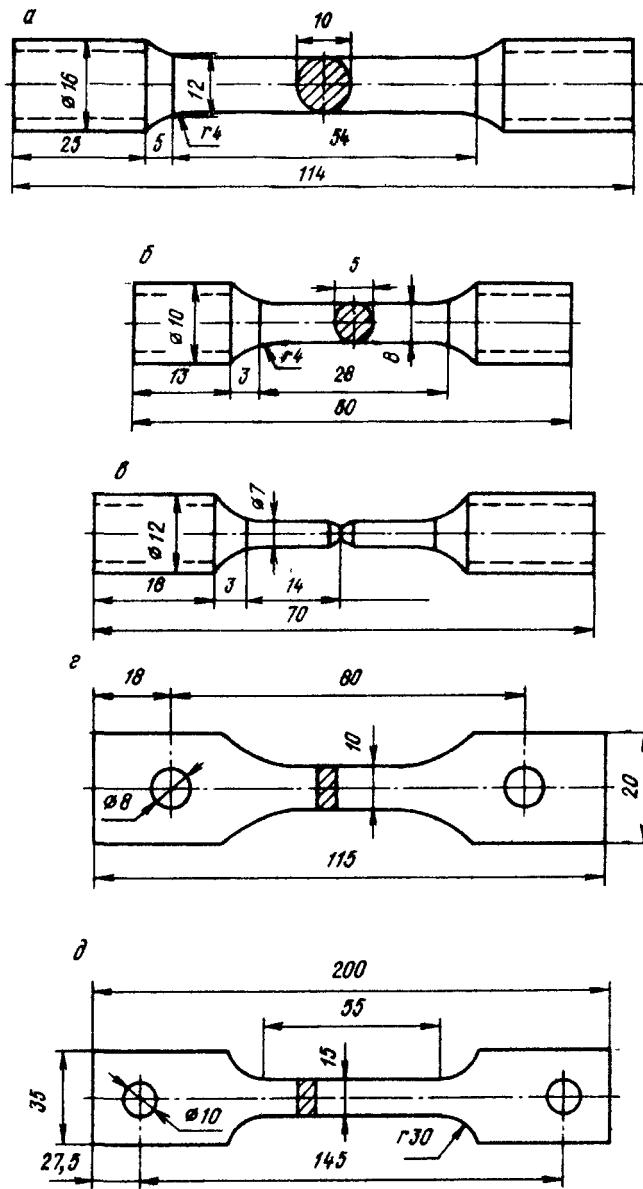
Форма и размеры образцов для испытания на ползучесть: а - цилиндрический укороченный; б - цилиндрический малый; в - с круговым надрезом; z - плоский малый; д - плоский
